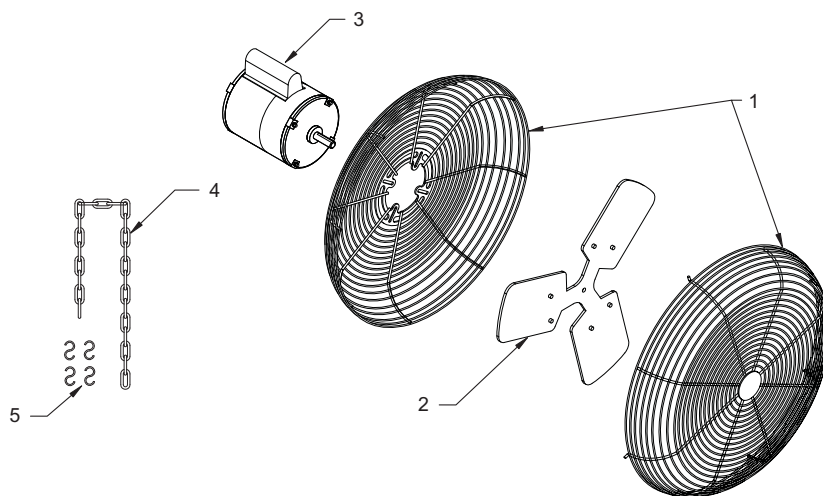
Pièces de rechange pour les ventilateurs industriels assemblés pour serres
